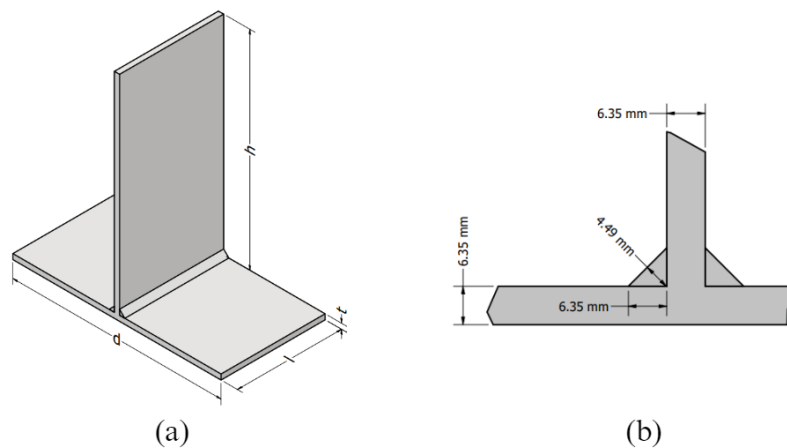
(a) Esquema geométrico do conjunto. (b) Detalhamento do cordão de solda do conjunto.
